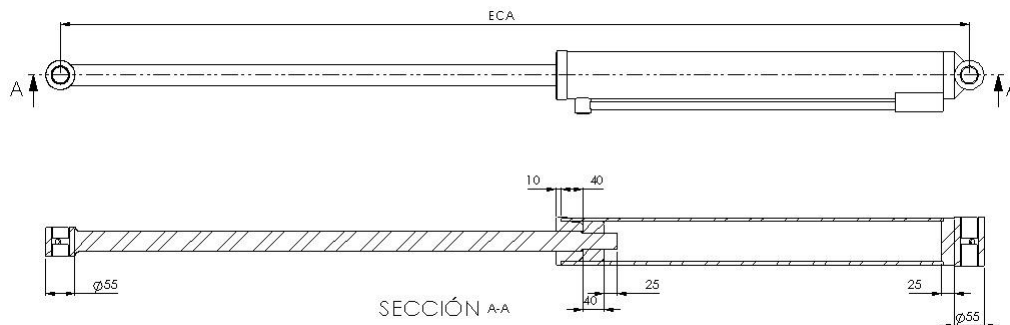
Dimensiones constructivas cilindro principal ECA
